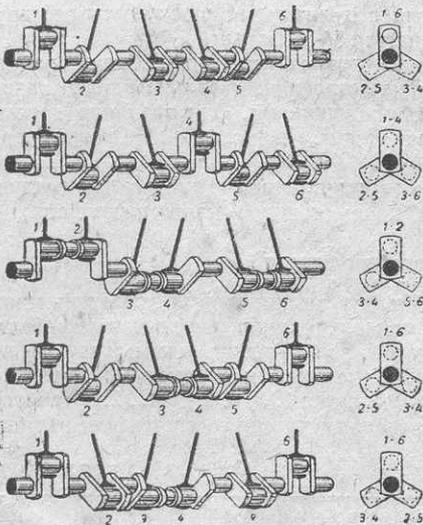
Расположение кривошипов вала шестицилиндрового двигателя.
